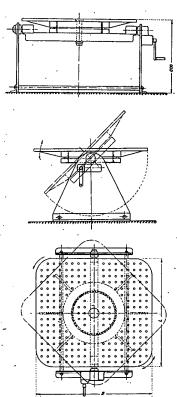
Universal-Schweißtisch (Wagner & Neher)
